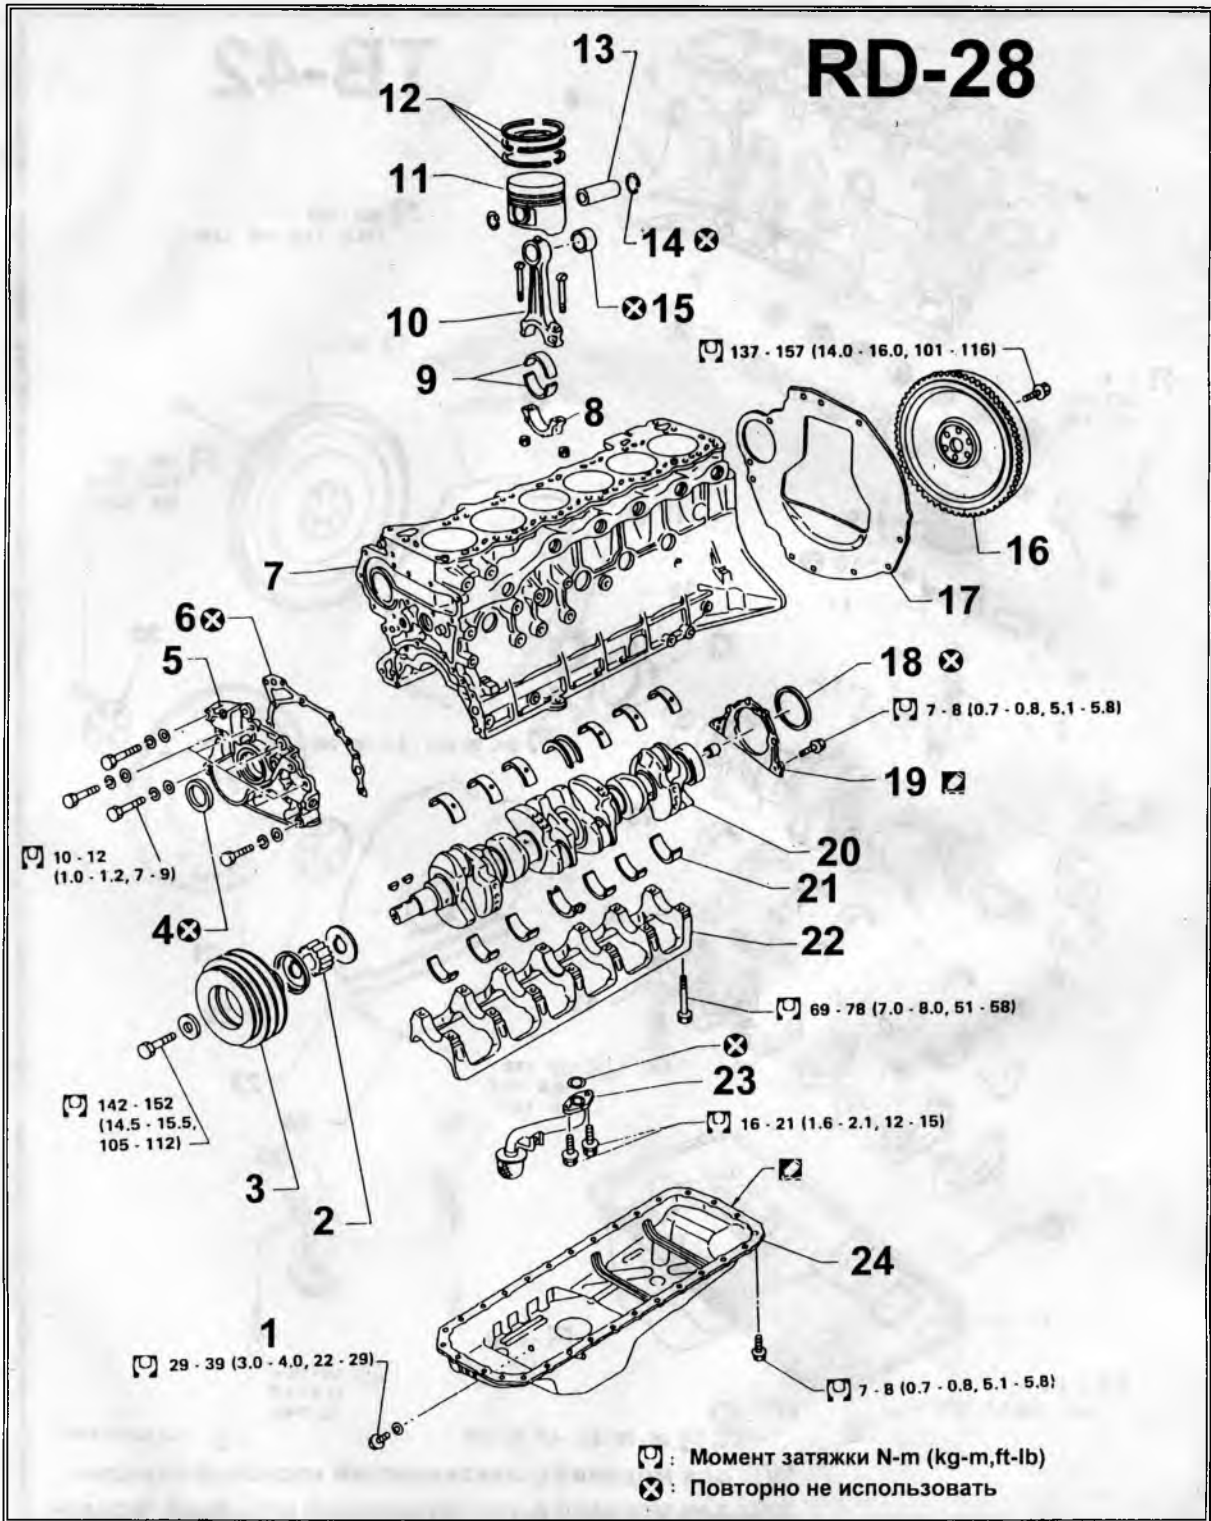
1. Сливная пробка. 2. Зубчатый шкив коленчатого вала. 3. Шкив коленчатого вала для клинового ремня. 4. Передний сальник коленчатого вала. 5. Масляный насос. 6. Прокладка масляного насоса. 7. Блок цилиндров. 8. Крышка шатунного подшипника. 9. Вкладыши шатунного подшипника. 10. Шатун. 11. Поршень. 12. Поршневые кольца. 13. Поршневой палец. 14. Стопорное кольцо. 15. Втулка малого конца шатуна. 16. Маховик. 17. Задняя (опорная) плита. 18. Задний сальник коленчатого вала. 19. Держатель сальника. 20. Коленчатый вал. 21. Коренные подшипники. 22. Крышка коренных подшипников. 23. Маслоприемник. 24. Поддон масляного картера.
